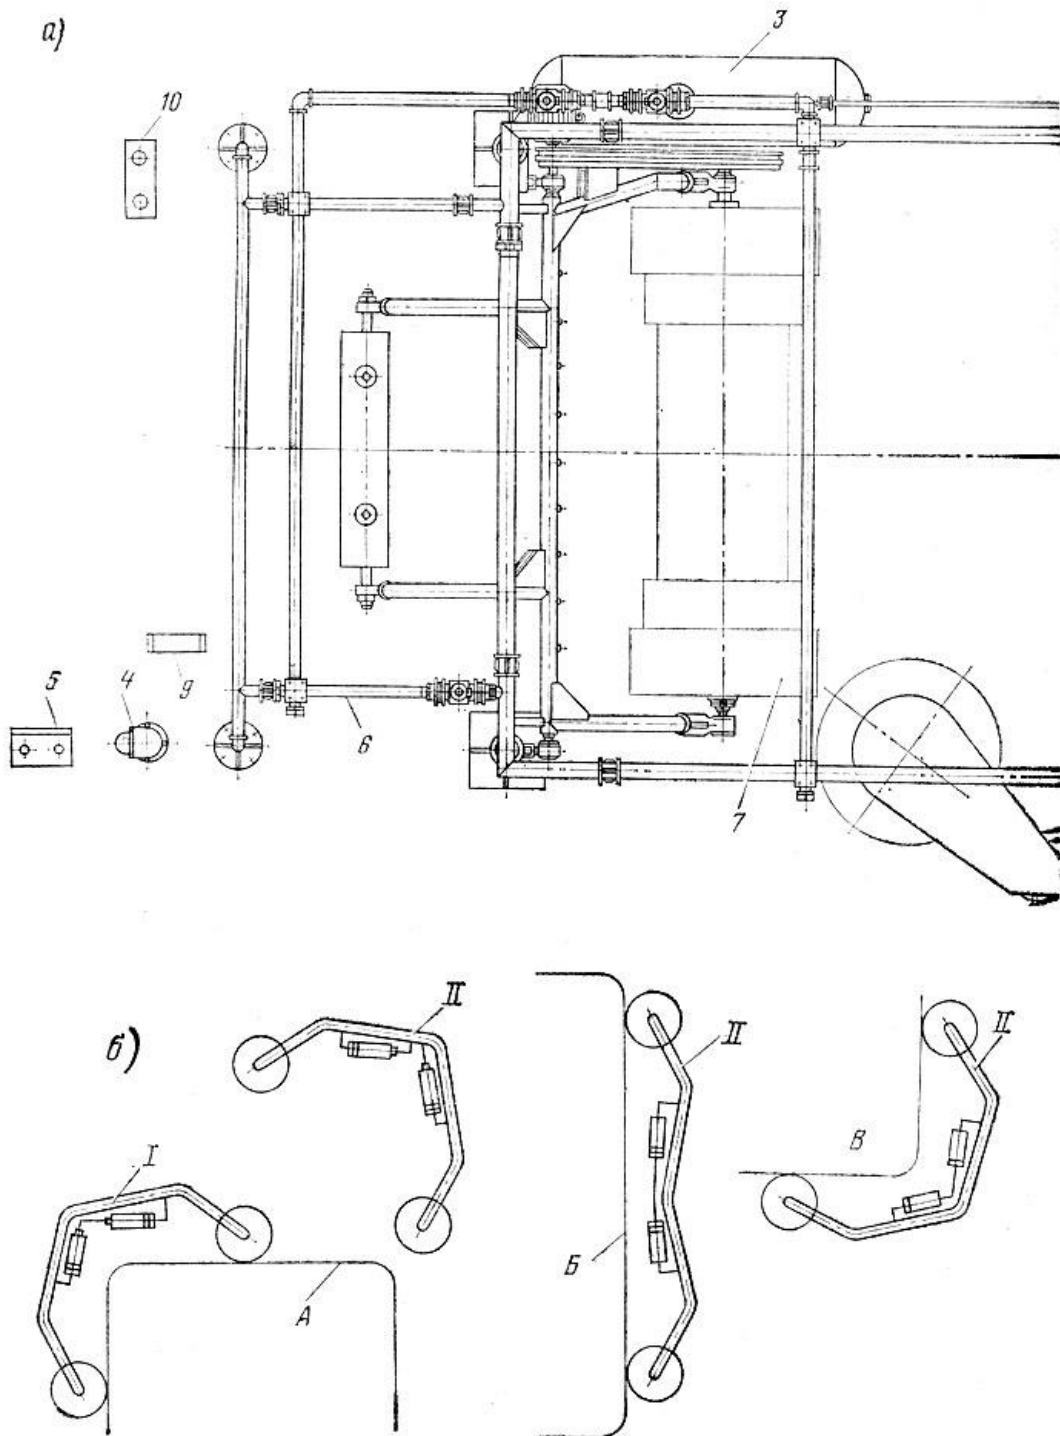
Установка для мытья модели ЦКБ-1126: а – загальний вигляд; б – схема роботи вертикальних щіток; 1 – тримна стійка каркаса; 2 – повітре-розподільний пристрій пневмосистеми установки; 3 – ресивер; 4 – командо-контролер; 5 – апаратна шафа; 6 – рамка попереднього змочування; 7 – горизонтальна щітка; 8 – рамка остаточного обмивання; 9 – педалі командо-контролерів; 10 – світлофор; 11 – рама каркаса; 12 – вертикальні щітки; 13 –
